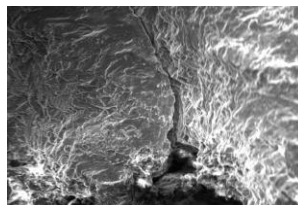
Внешний вид излома образца сплава АМг6 с биокоррозионными поражениями после испытаний на циклическую усталость. (Усталостная трещина начала развиваться от биокоррозионного повреждения)
